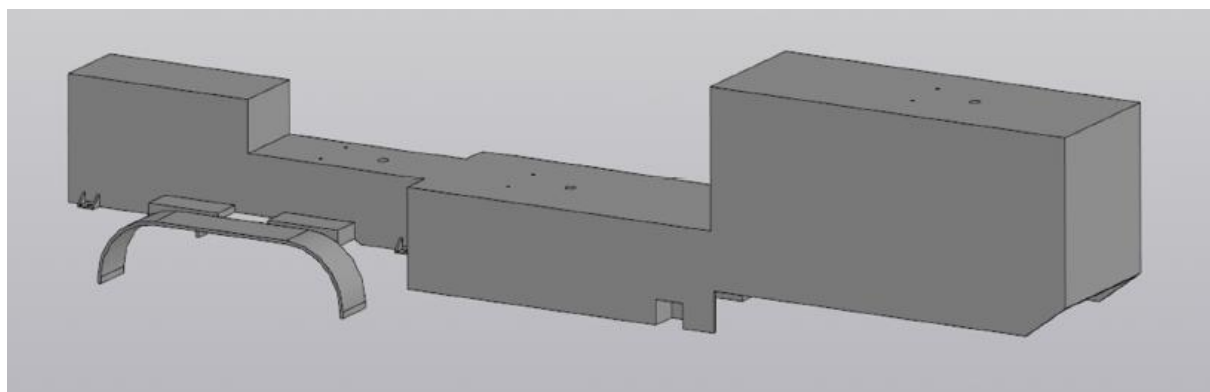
3D-модель части корпуса, накрывающей полуприцеп
